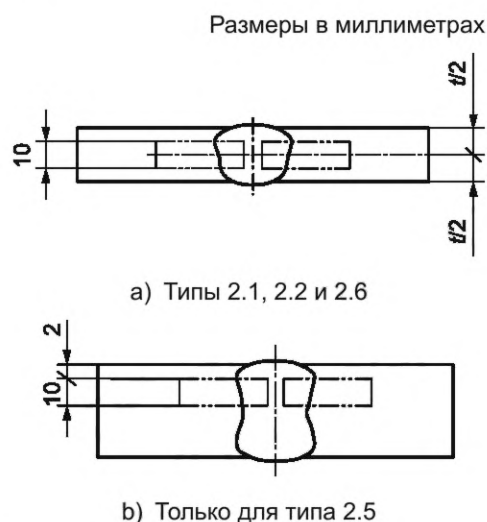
Расположение образцов для испытаний на ударный изгиб
